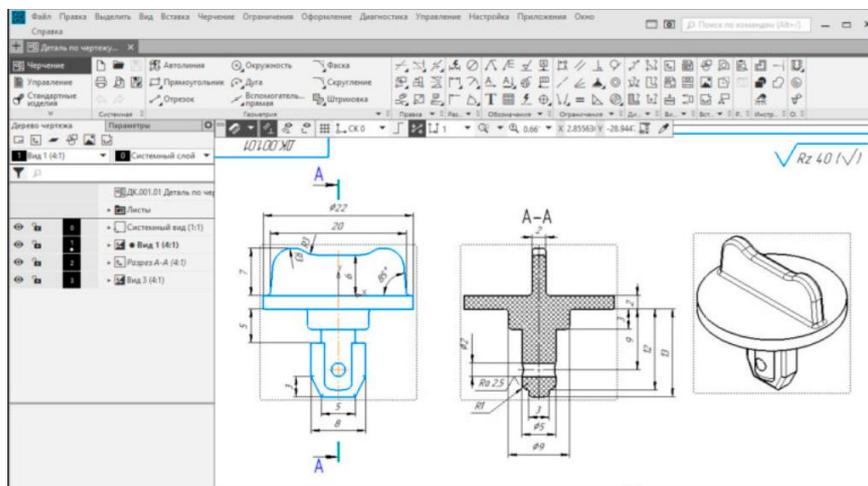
рабочий чертеж детали в КОМПАС-3D
